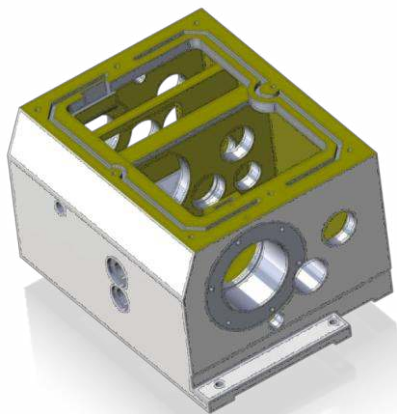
Корпус шпиндельной бабки станка с ЧПУ TC1625Ф3 (Россия)
